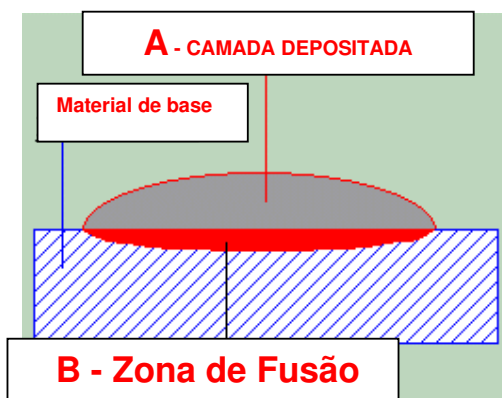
Diluição por técnica de soldagem (MARCONI, 2002).
